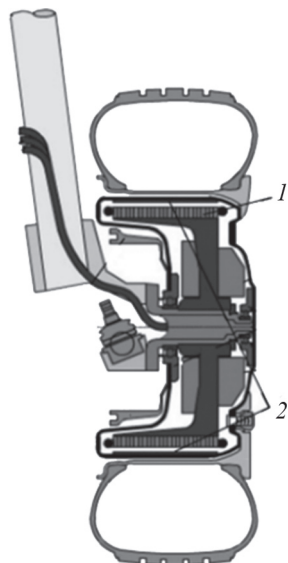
Мотор-колесо: 1 – статор; 2 – ротор
